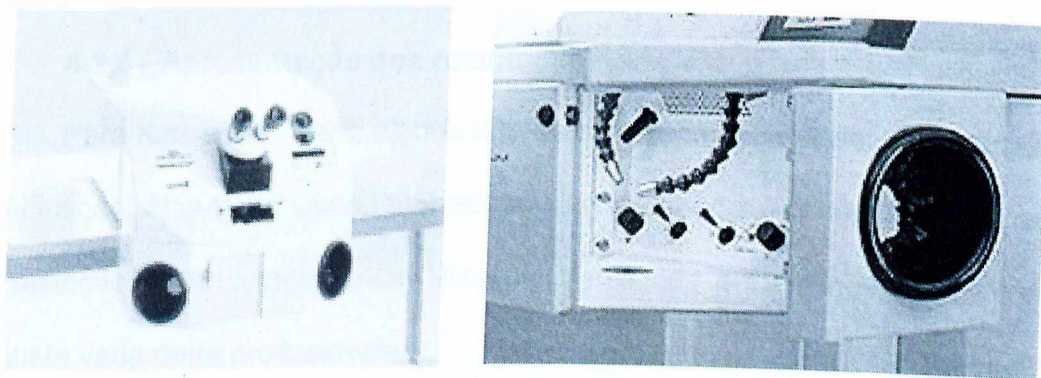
Foto ilustrativa do aparelho de soldagem a laser, com detalhe para a região de soldagem, aparelho Desktop.
